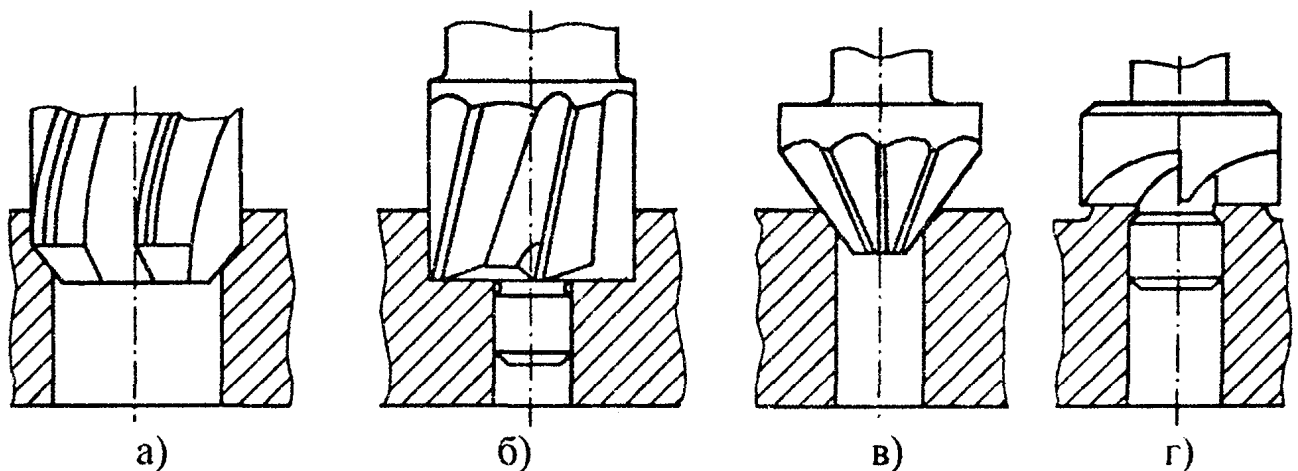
Типы зенкеров: а) – цилиндрический зенкер; б, в, г – зенковки.
